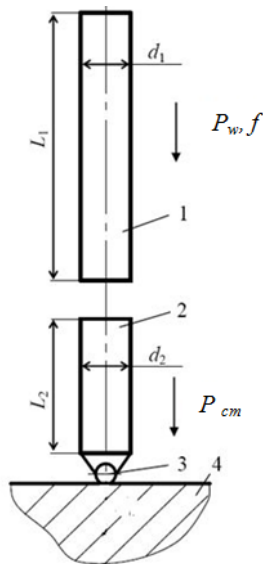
Схема ударної системи бойок-інструмент гладкої циліндричної форми
